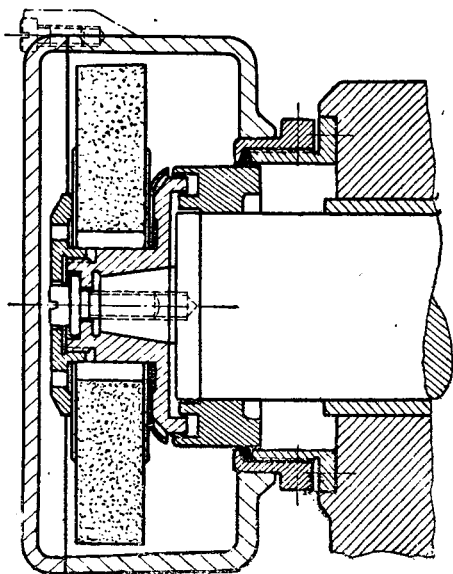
Крепление шлифовального круга на шпинделе станка Шток, тип ВN-I.
